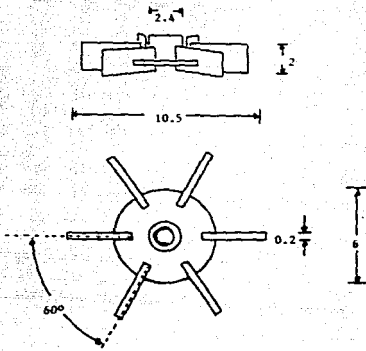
DIMENSIONES DEL AGITADOR DE TURBINA HOJAS RECTAS
